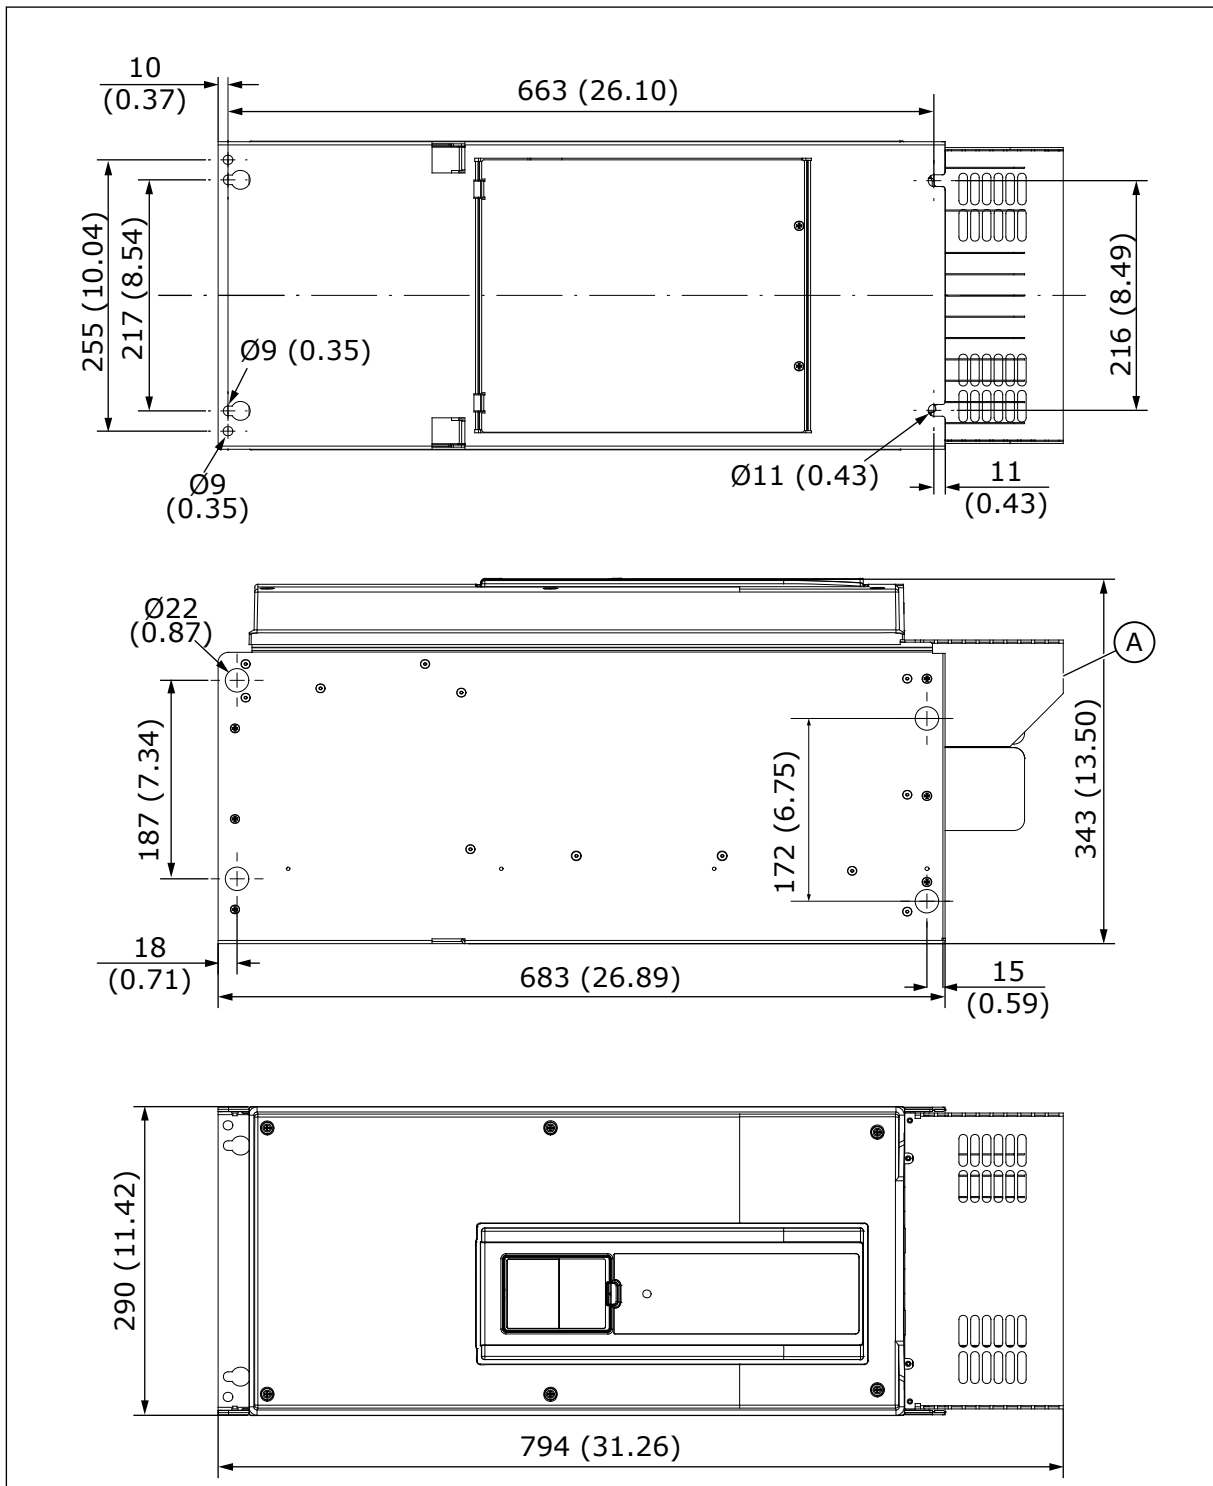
Dimensioni dell'inverter, MR8 [mm [pollici]]
